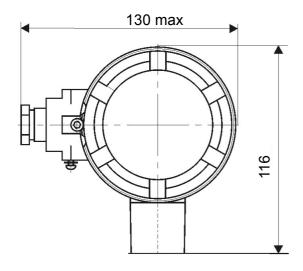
НПТ-1Ц.Г.КВ в корпусе
